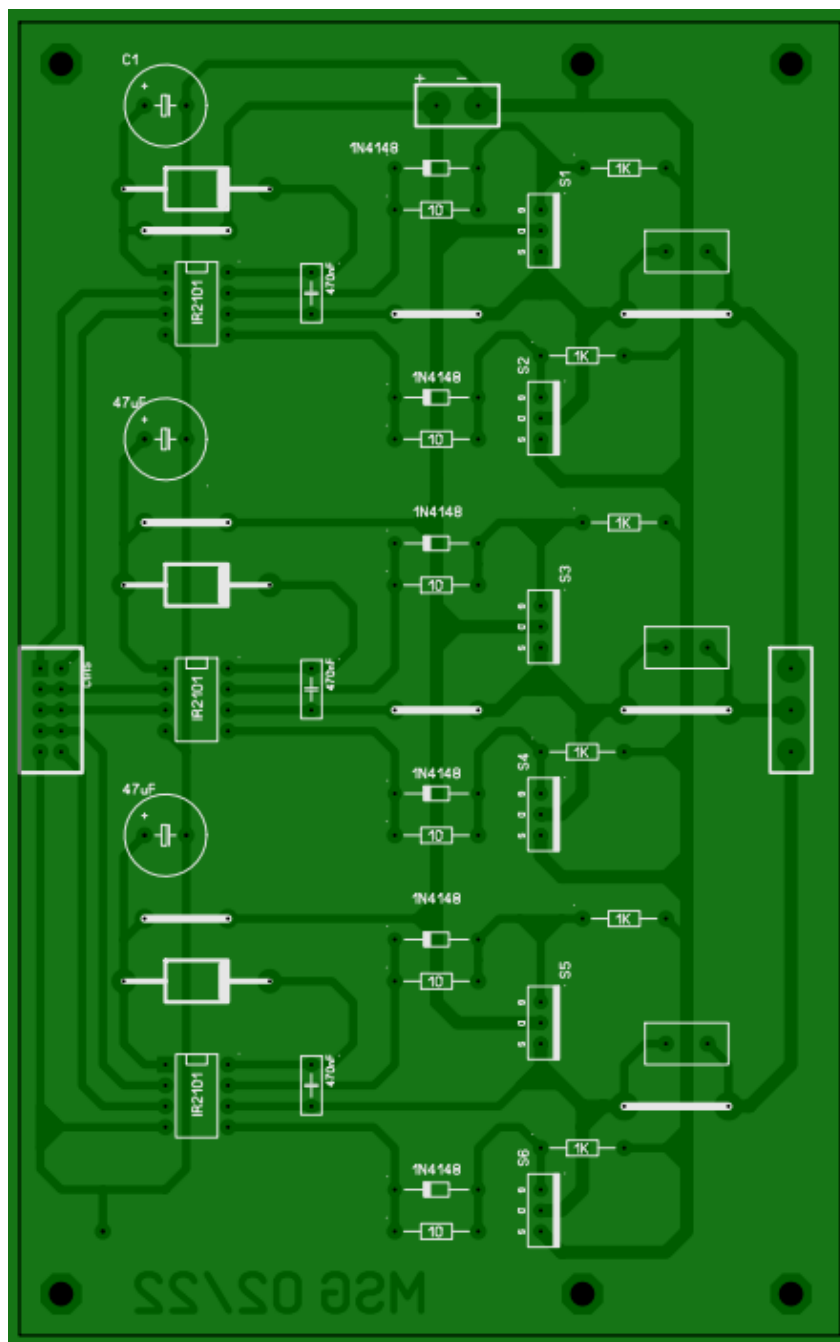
Vista de componentes del diseño de la PCB de potencia. Fuente [Propia]
